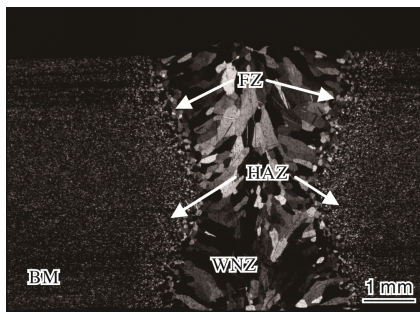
金属钪真空电子束焊缝的横截面形貌
